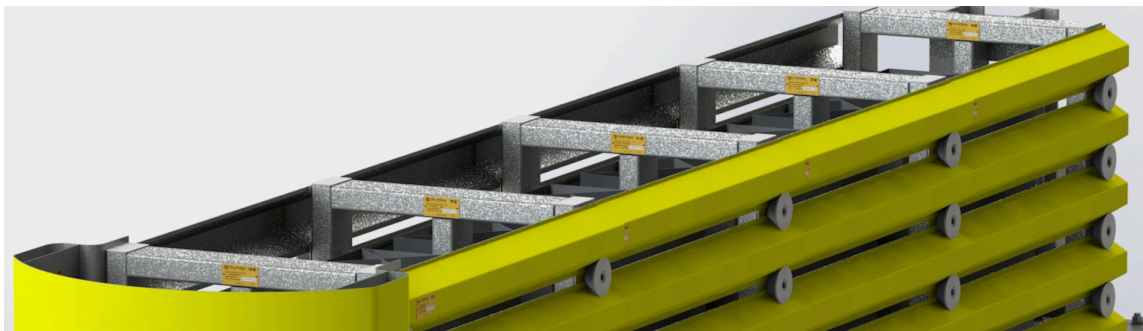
расположение маркировочной бирки на силовых рамах.
